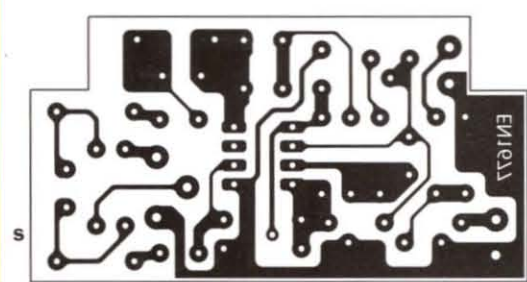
A Dessin, à l'échelle 1, du circuit imprimé coté soudure.
